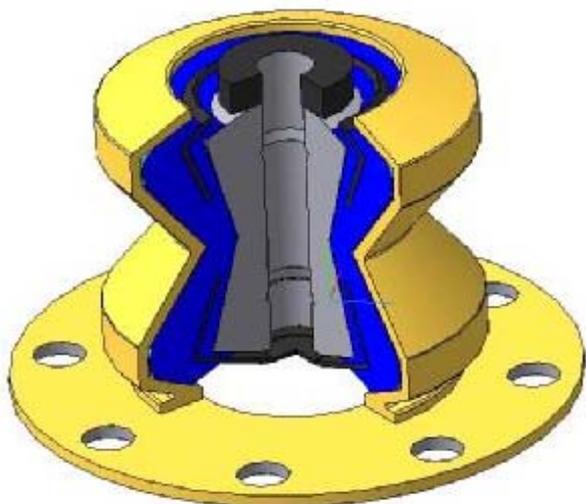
Общий вид разработанной виброизолирующей опоры с корпусом, привариваемым к основанию
